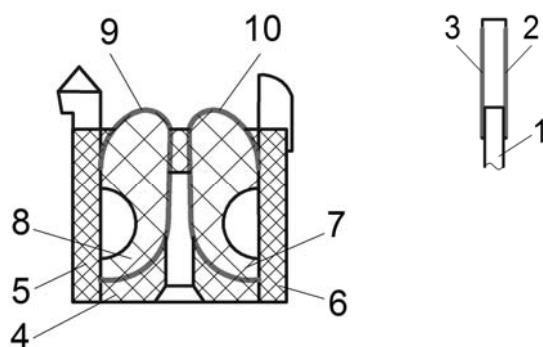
Конструкция соединителя с двухсторонним расположением контактов:
